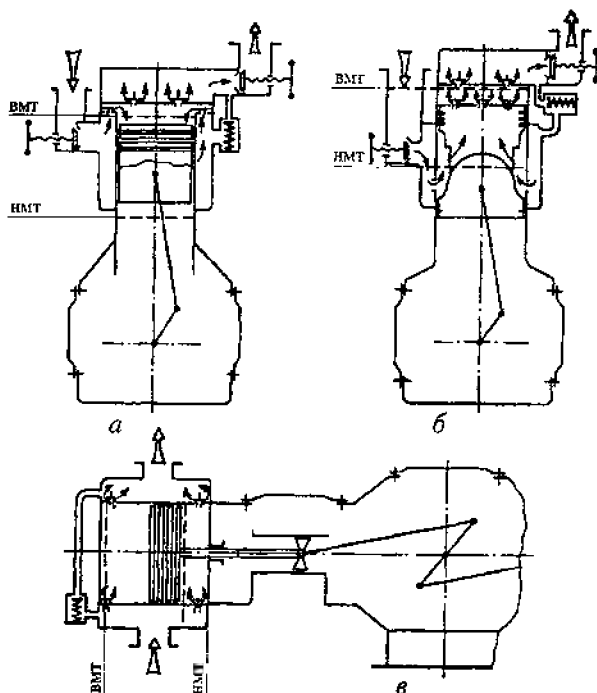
Схемы поршневых холодильных компрессоров [32]:
